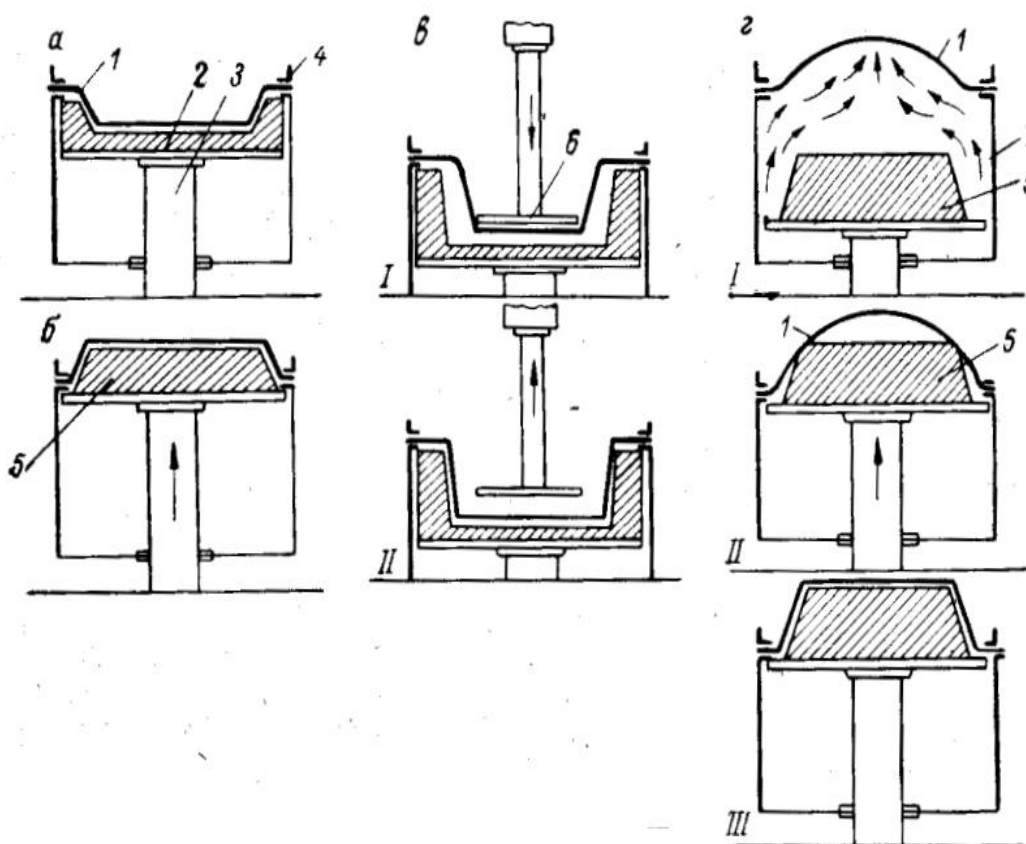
Примеры методов вакуумного термоформования: а — в негативной форме; б — в позитивной форме; в — с предварительной вытяжкой заготовки пуансоном; г — с предварительной пневматической вытяжкой заготовки. 1 — заготовка; 2 — негативная форма; 3 — стойка; 4 — зажимная рама; 5 — позитивная форма; 6 — пуансон; 7 — формовочная камера; I–III — позиции формования
